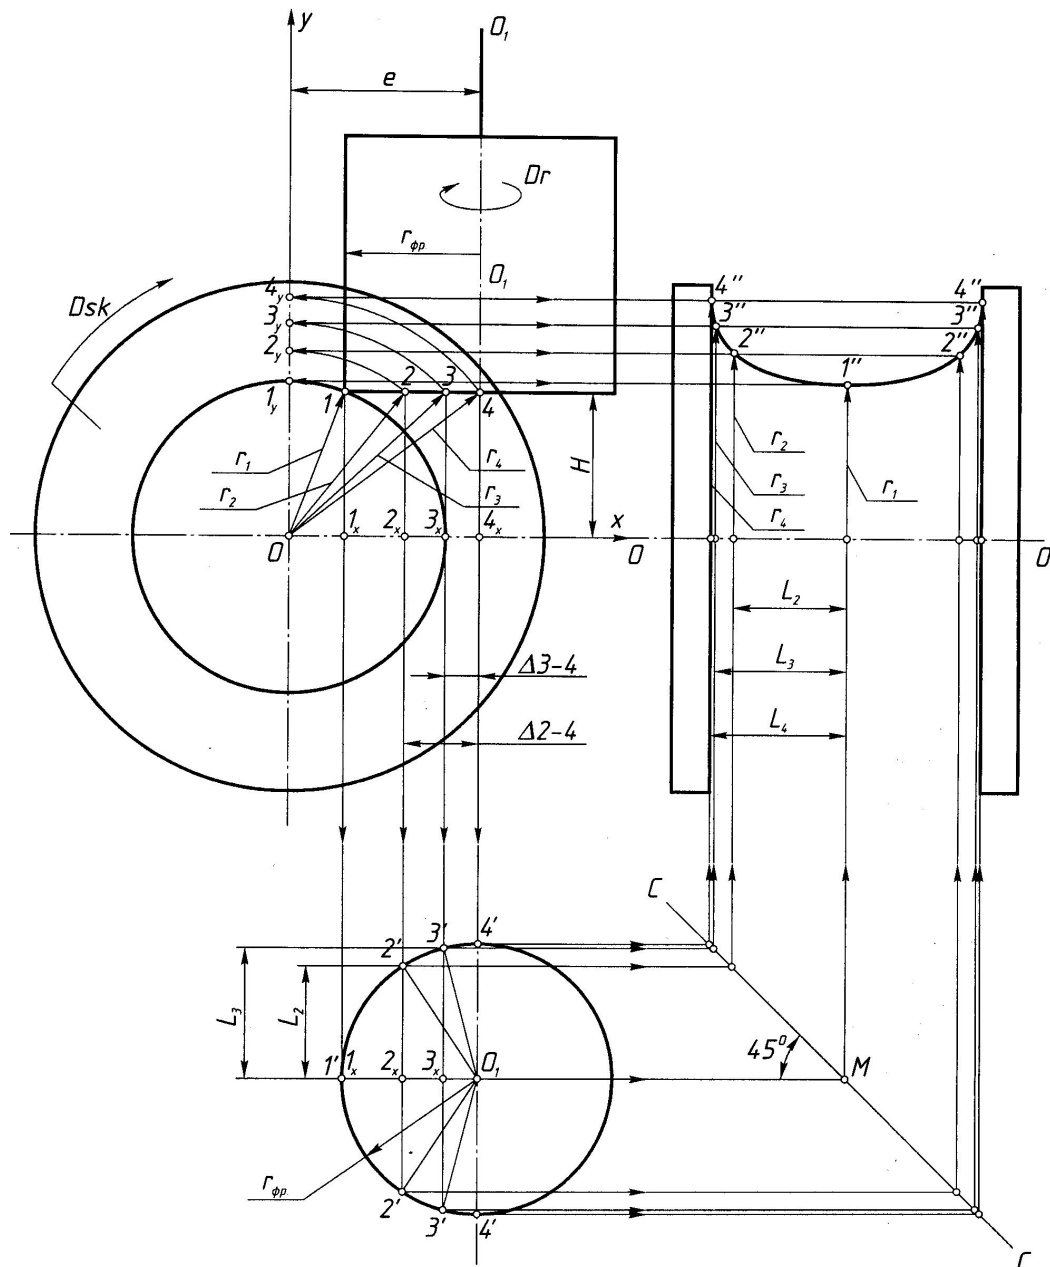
Схема обробки кільцевої канавки на периферії заготовки тангенціально зміщеною кінцевою фрезою.
